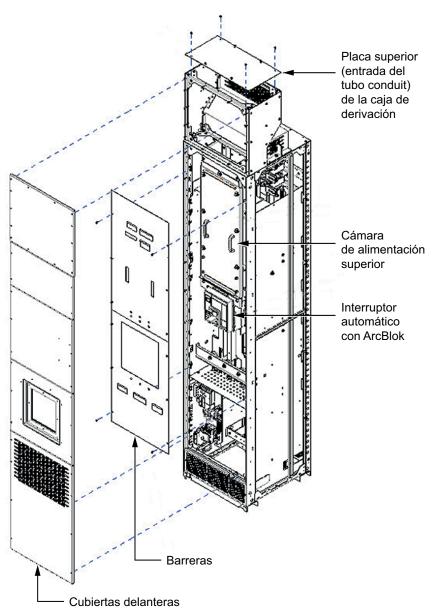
Acceso a la cámara de cables con aislamiento del lado de línea y al interruptor de zapata principal del ArcBlok con alimentación en la parte superior
